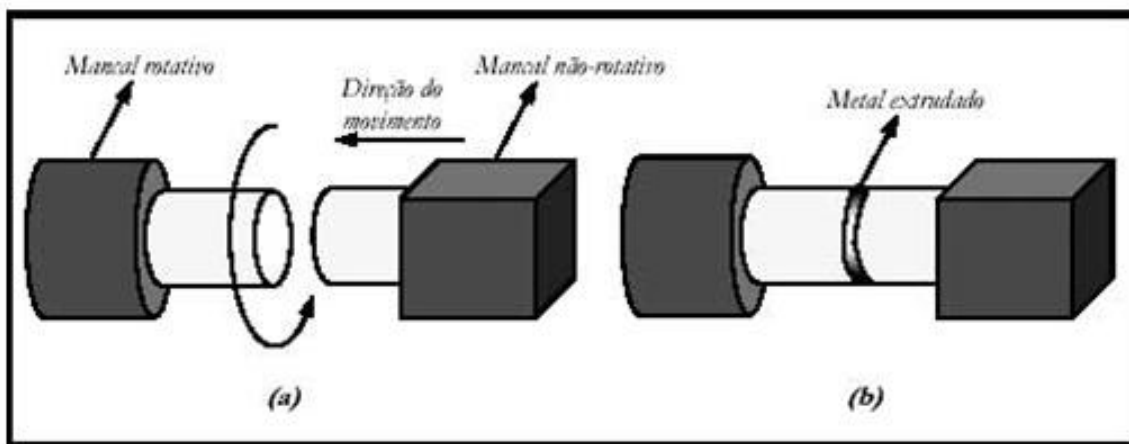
Representação esquemática do processo de soldagem por fricção: (a) mancal aproximando-se e (b) após soldagem.
